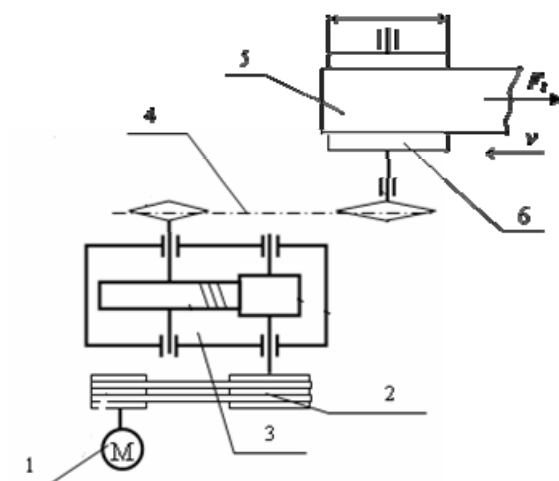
Схема привода ленточного конвейера: 1 – электродвигатель; 2 – ремённая передача; 3 – редуктор цилиндрический одноступенчатый; 4 – цепная передача; 5 – лента конвейера; 6 – барабан конвейера
